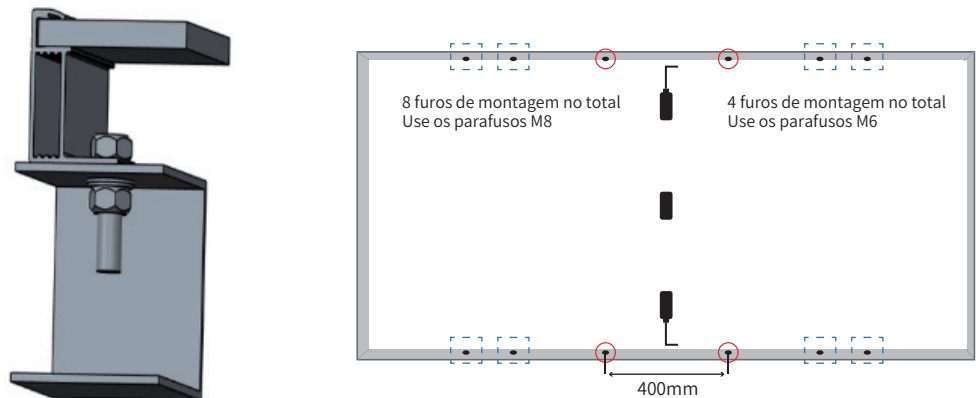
Diagrama de instalação do furo de montagem de componente lado único
